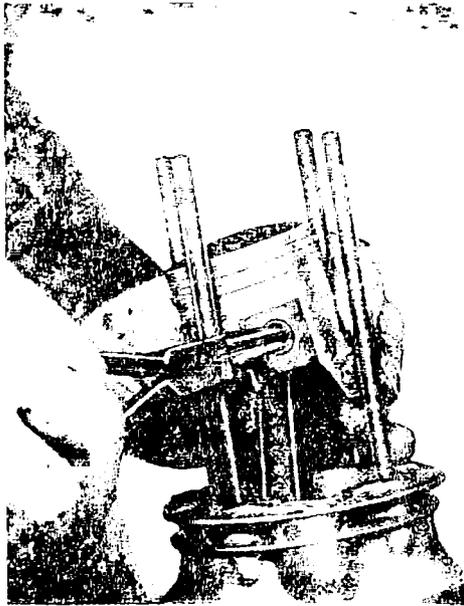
Entfernen der Kolbenbolzen-Sicherungen mit Seegerzange Nr. 0997
